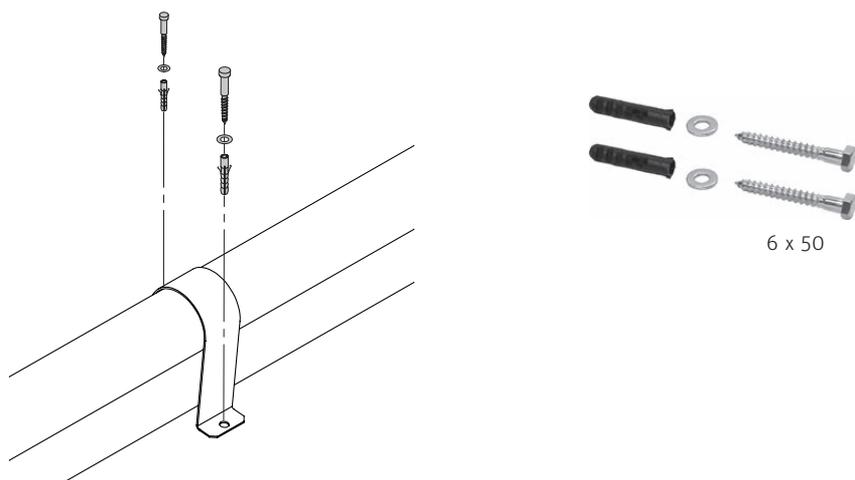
Fissare i tubi e le fascette nella stiva di stoccaggio
